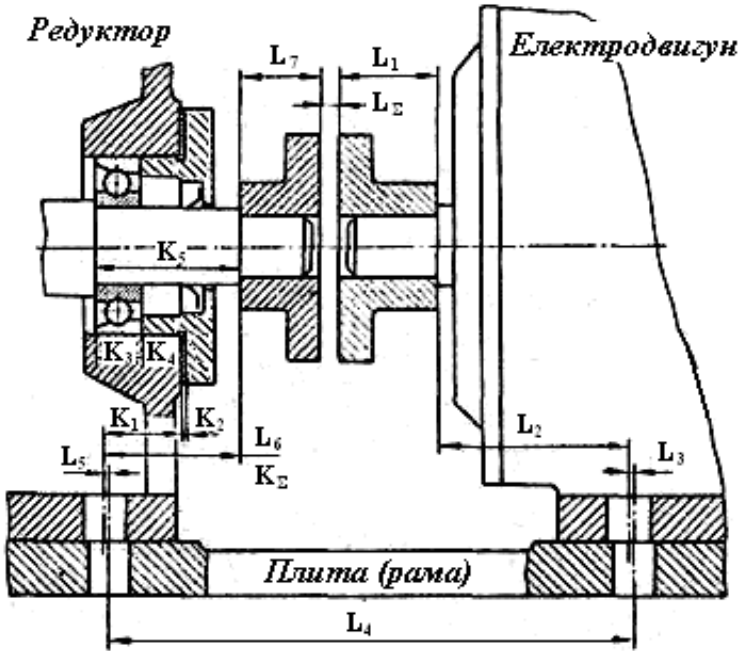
Структура розмірної ланки осьового розташування валів електродвигуна і редуктора
